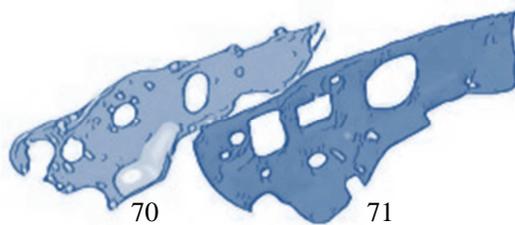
Módulo 8 –Sensor Solar- Cockpit. Fuente Propia.
